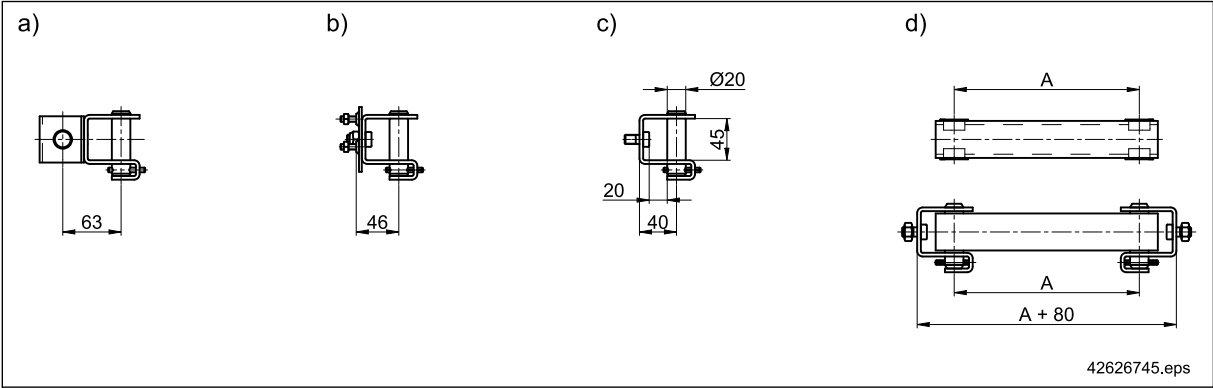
Bauteile Abstandhalter mit Gelenken, kurvengängig
